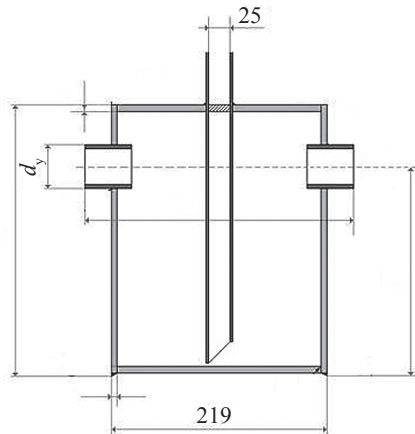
Схема конденсатосборника с габаритными размерами
